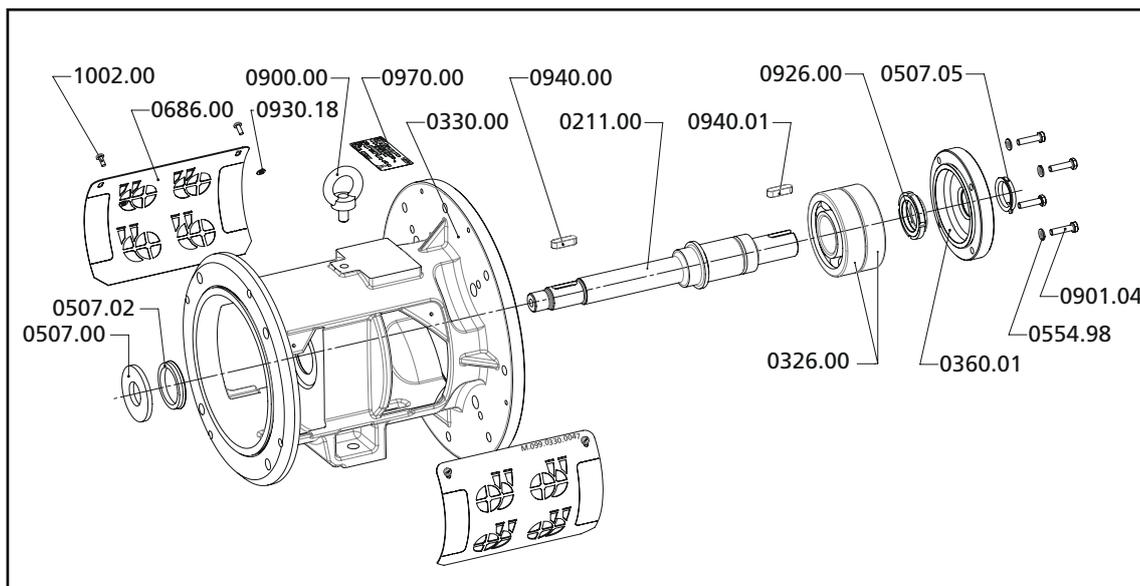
Supporto cuscinetto sino a dimensione motore IEC 160 (NEMA 256T)
